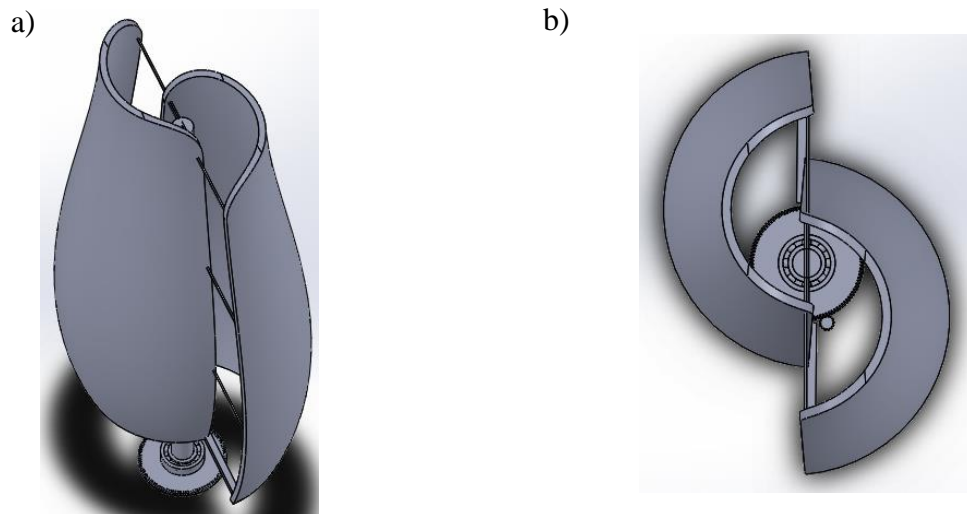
Ensamblaje de la turbina eólica de Tulipán sin el anillo difusor. a) vista lateral, b) vista superior. Diseñada con SolidWorks®.
